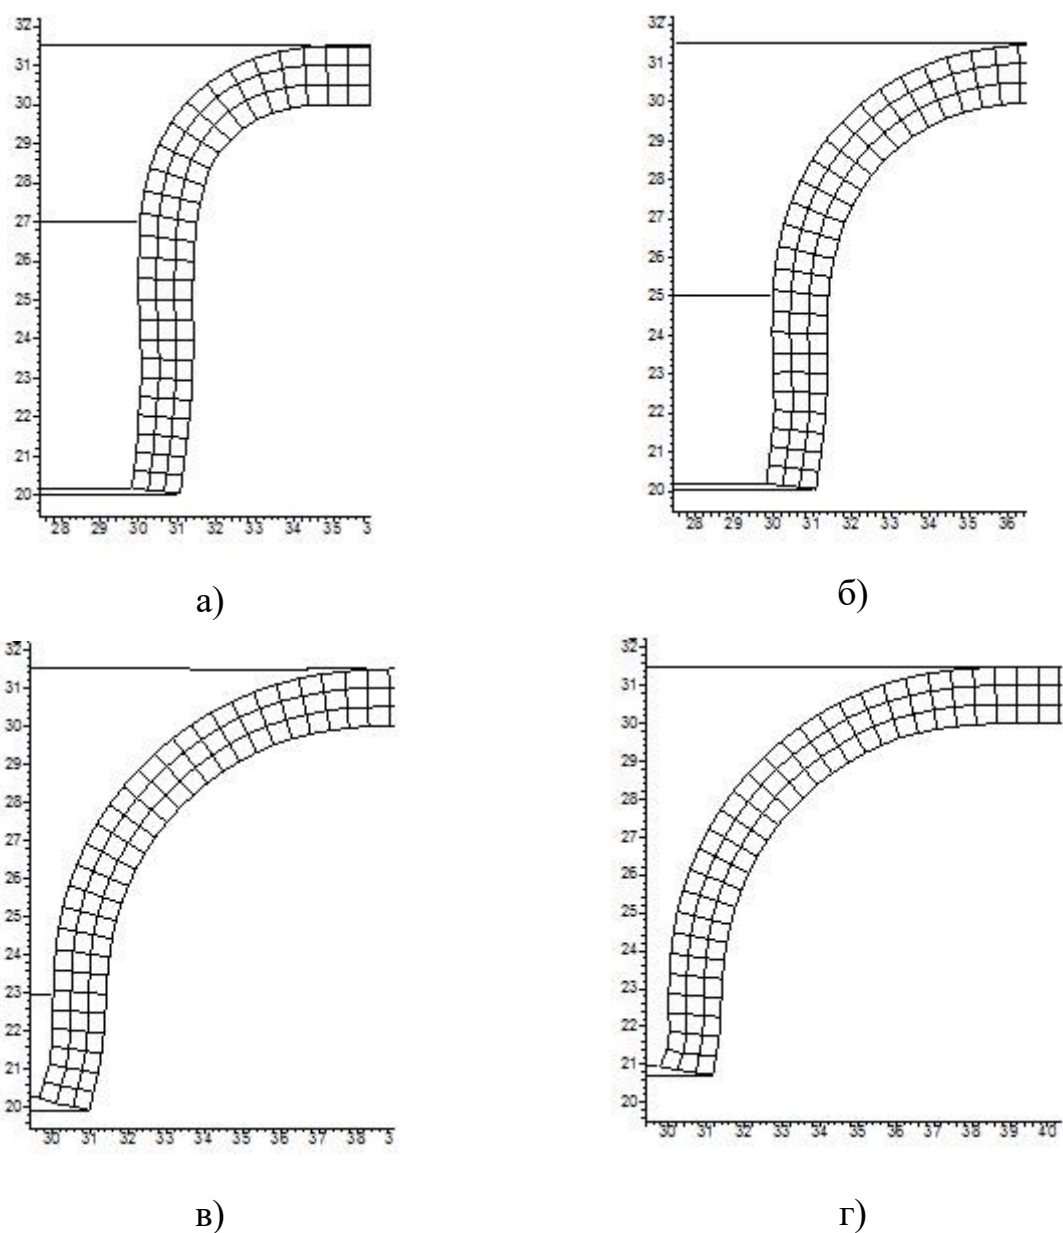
Геометрическая форма сдеформированной части заготовки после отбортовки с учетом определенной упругой деформации и упрочнения:
